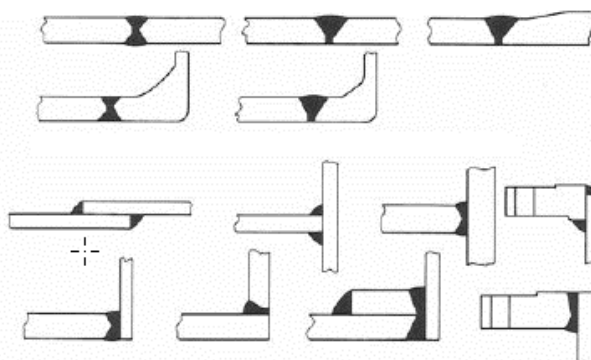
Soldas de inspeção fácil por radiografia. TELLES, 2001.
